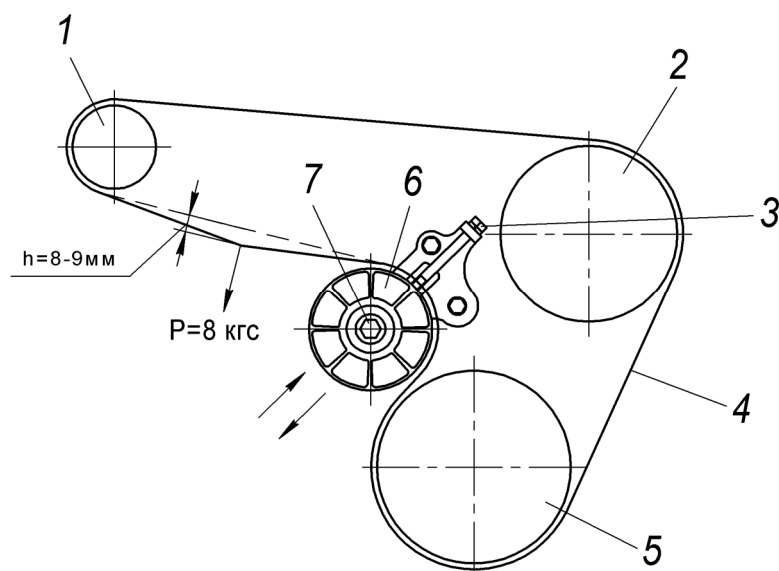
Схема натяжения ремня привода агрегатов:
